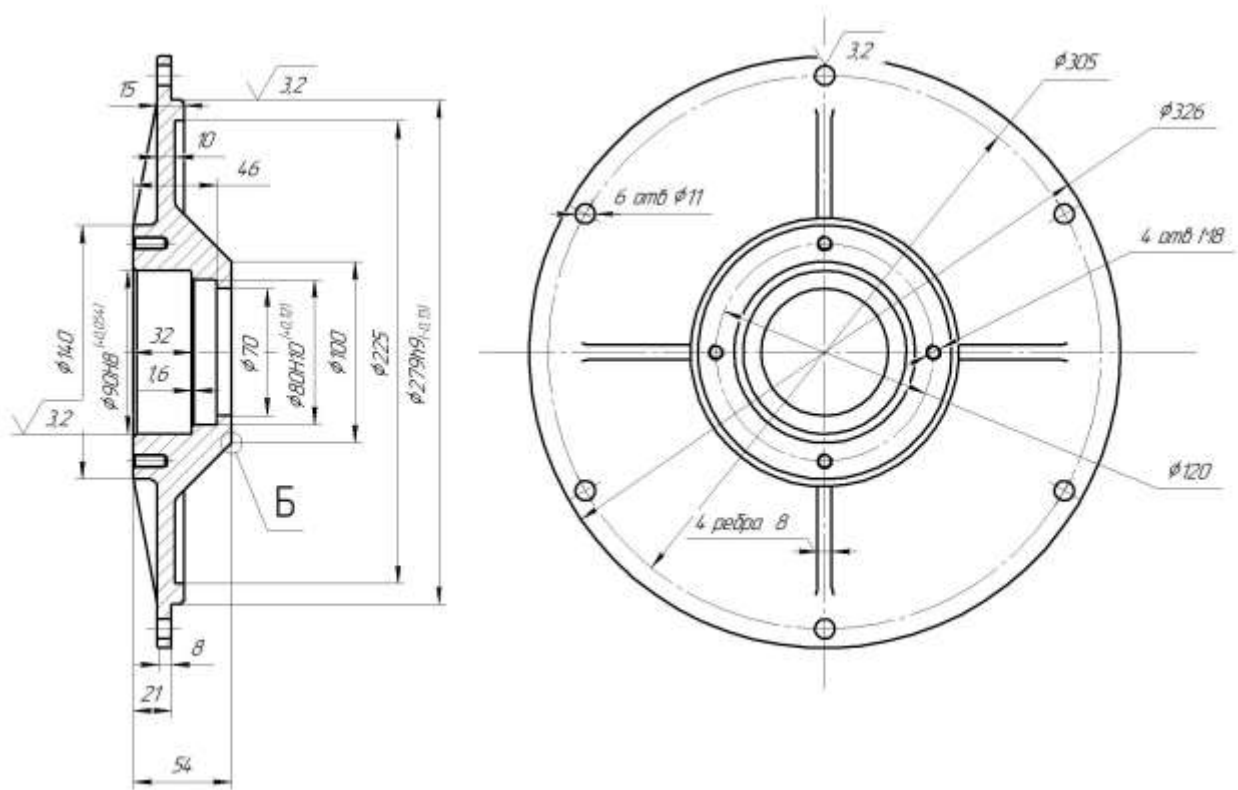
Деталь «Кришка редуктора КС6Б-0.01»
